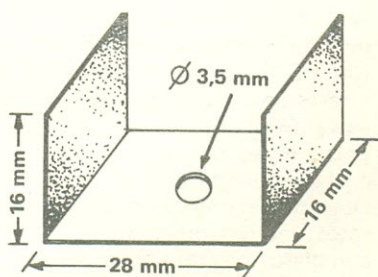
Desenho e dimensões do dissipador do transistor de potência. Utilizar chapa de alumínio de (pelo menos) 2 mm de espessura.
